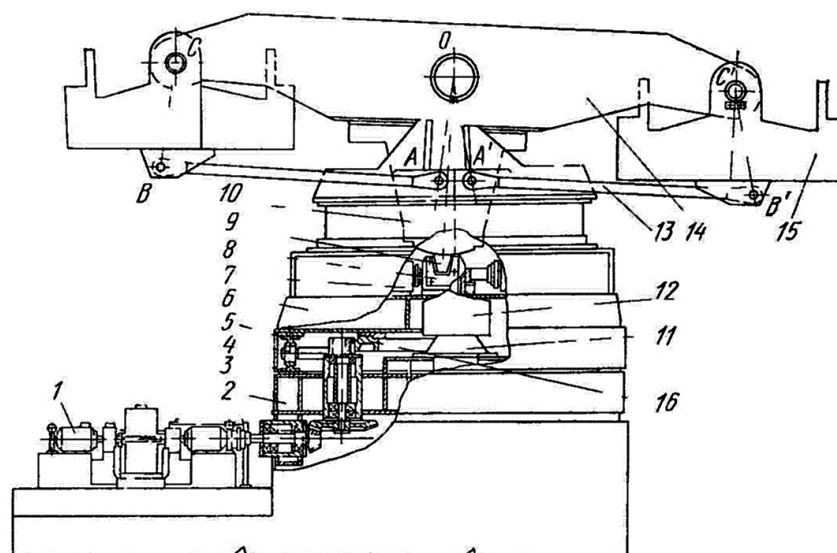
Поворотний сталерозливний стенд конструкції УЗТМ
